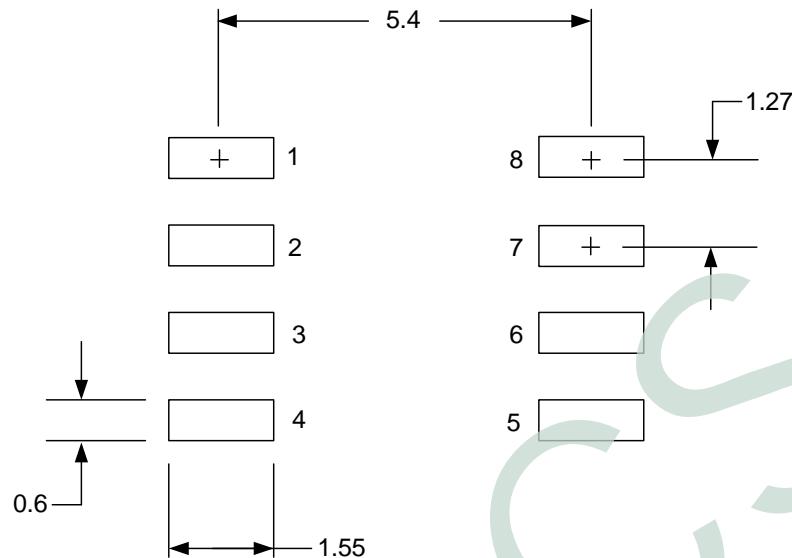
PCB 焊盘: SOP-8L (150 mil)
